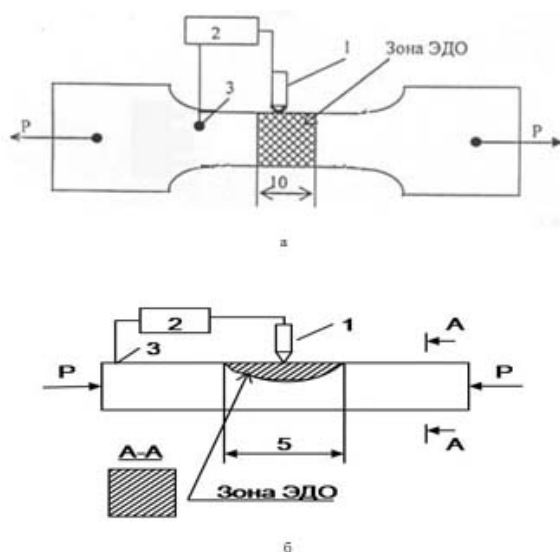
Схема обработки ИЭТ образцов алюминиевых сплавов, где: 1 — рабочий инструмент (электрод), 2 — конденсаторная машина, 3 — клемма контактного провода; образец типа "лопатка" для ЭДО в условиях упругого растяжения (а), прямоугольный образец для ЭДО в условиях упругого сжатия (б)
